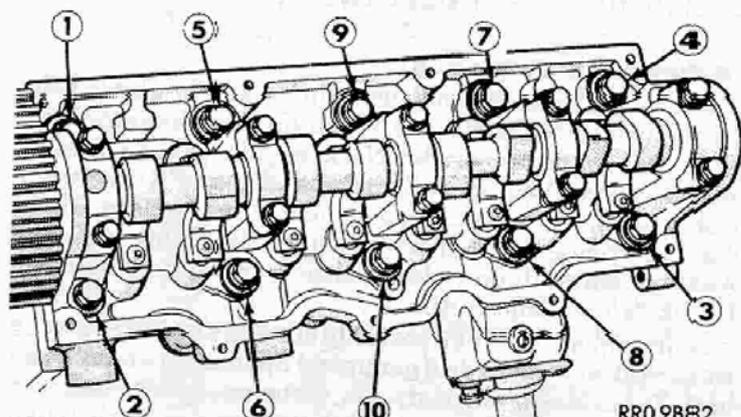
Reihenfolge beim Ausbau der Zylinderkopfbefestigungsschrauben
